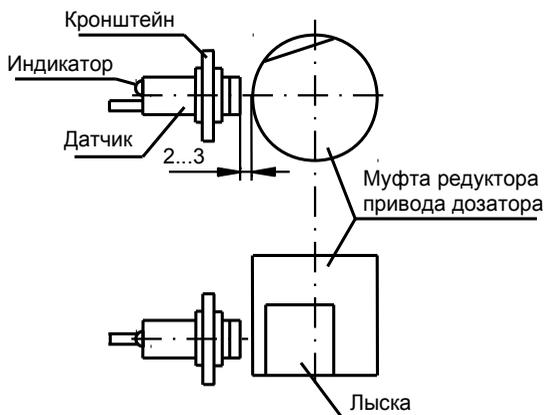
Регулировка рабочего зазора датчика дозатора
